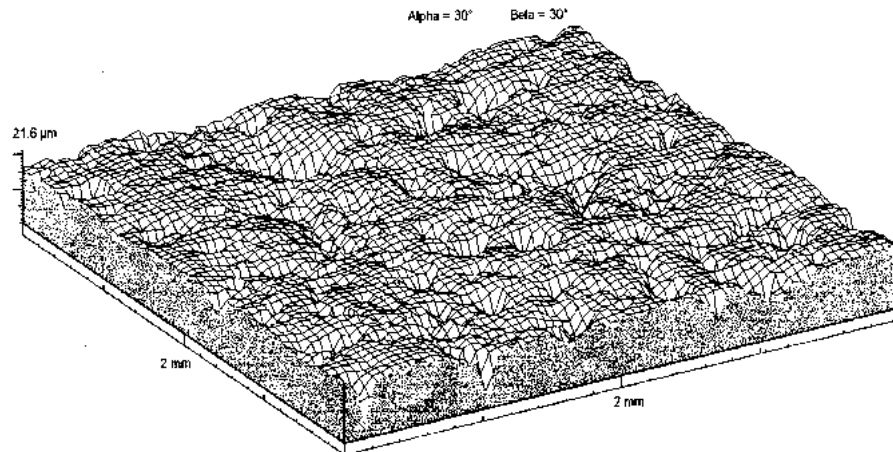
Аксонометричне зображення поверхні деталі після фрезерування та віброобробки у машині з центральним активатором руху робочого середовища
